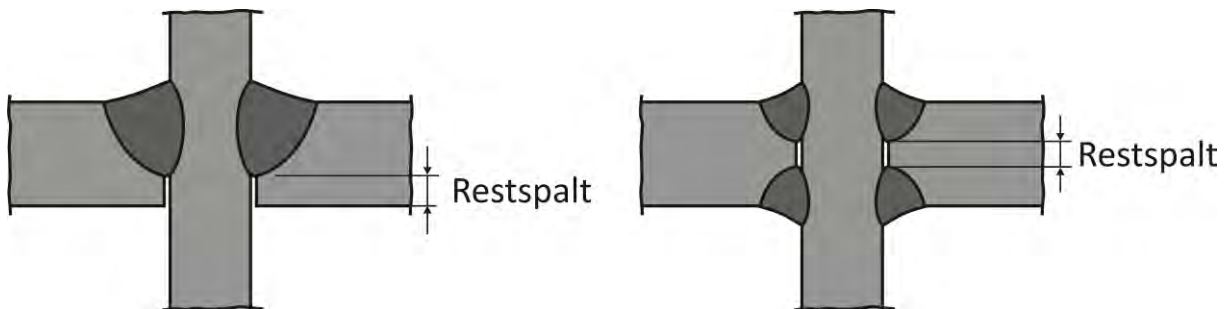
HV- bzw. DHV-Schweißstoß mit Restspalt bei Kreuzstößen
